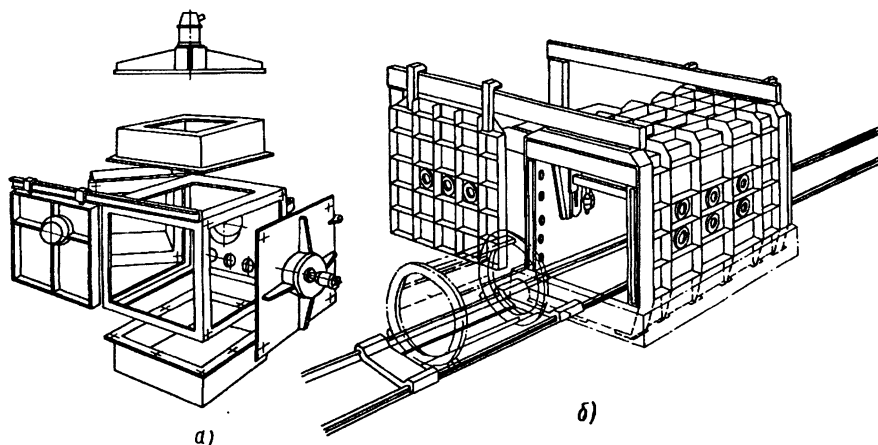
Прямоугольные сварочные камеры
